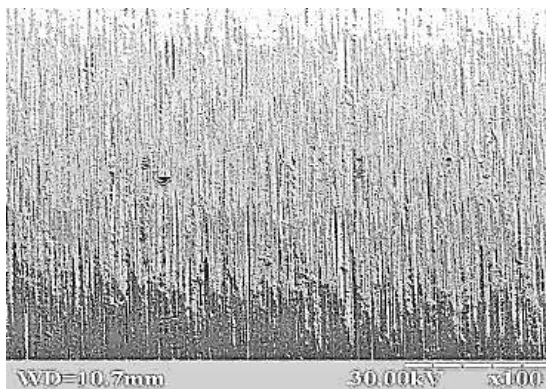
Типові частинки на поверхні деталі після шліфування
